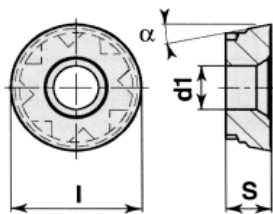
Твердосплавная пластина RPHX1605SN-T
